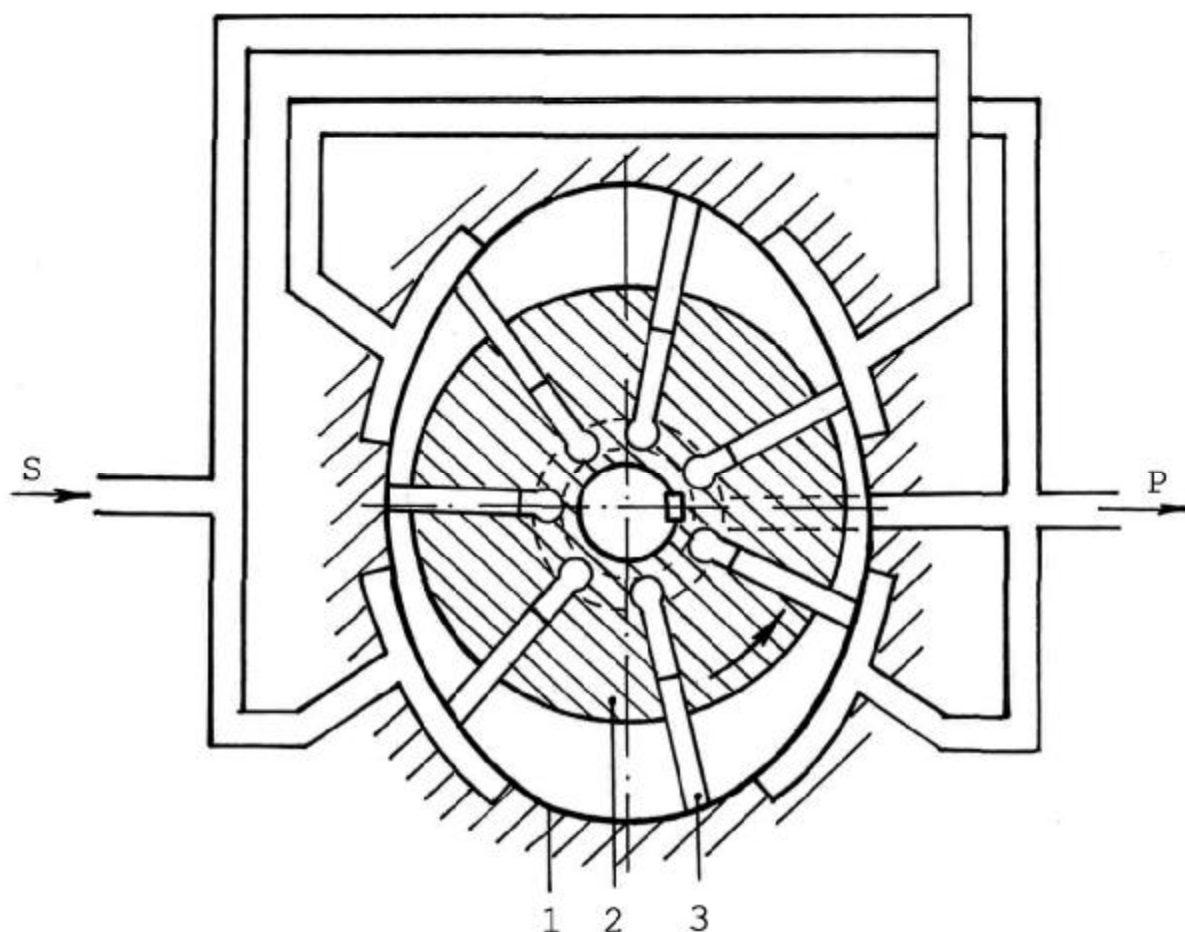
Кинематическая схема пластинчатой гидромашин двукратного действия: 1 – внутренняя поверхность статора; 2 – ротор; 3 – пластины.
